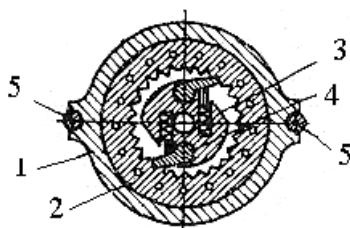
Поворотный механизм с двумя собачками в корпусе: 1 — букса; 2 — храповое кольцо; 3 — пружина; 4 — храповой стержень; 5 — болт.
